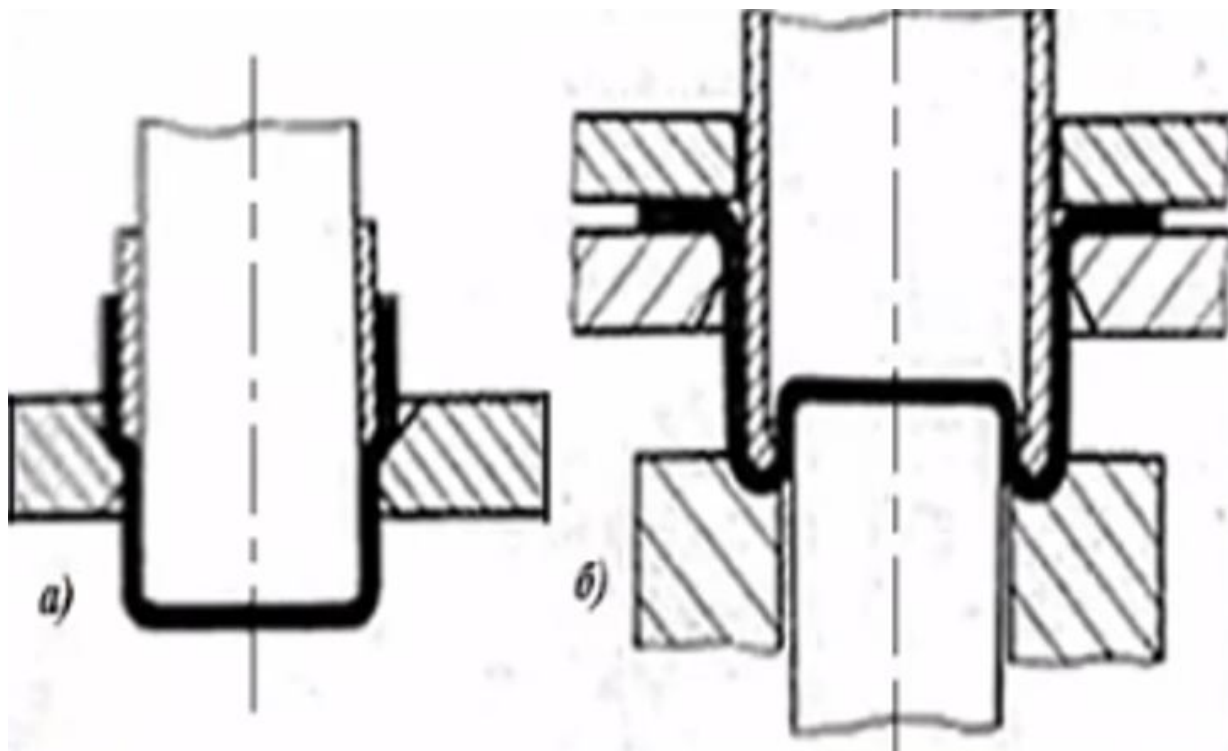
Схема витяжки порожнистої деталі з порожнистої заготовки: а) – двопозиційна витяжка; б) – зворотна витяжка.
